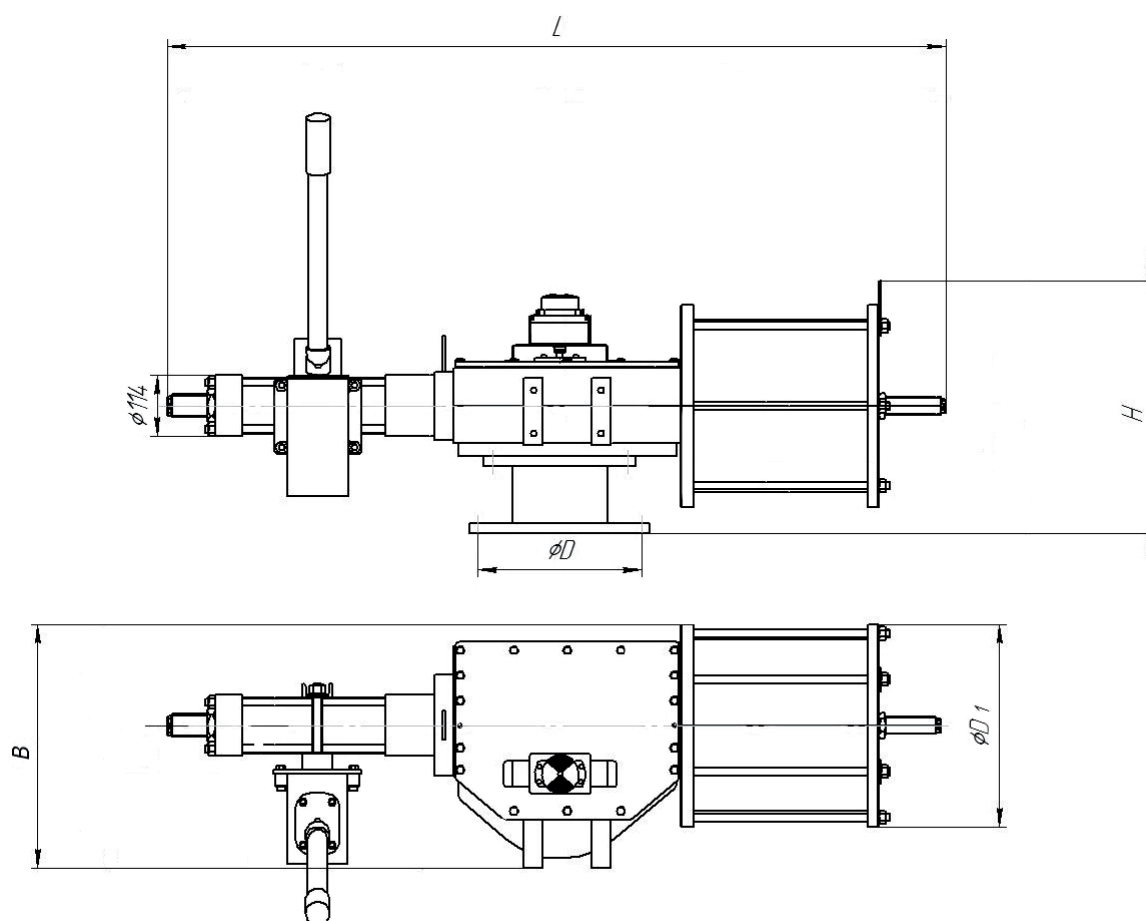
Общий вид пневмогидравлического привода ППГТ с габаритными и установочными размерами
